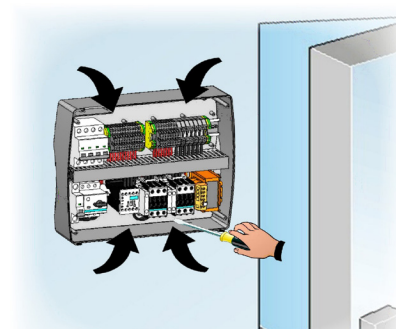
Unter Verwendung der vier zuvor hergestellten Löcher die Gehäuserückwand mithilfe von vier Schrauben, deren Länge für die Dicke der Wand geeignet ist, befestigen. Legen Sie zwischen jede Befestigungsschraube und die Gehäuserückwand eine der mitgelieferten Gummi-Unterlegscheiben.
